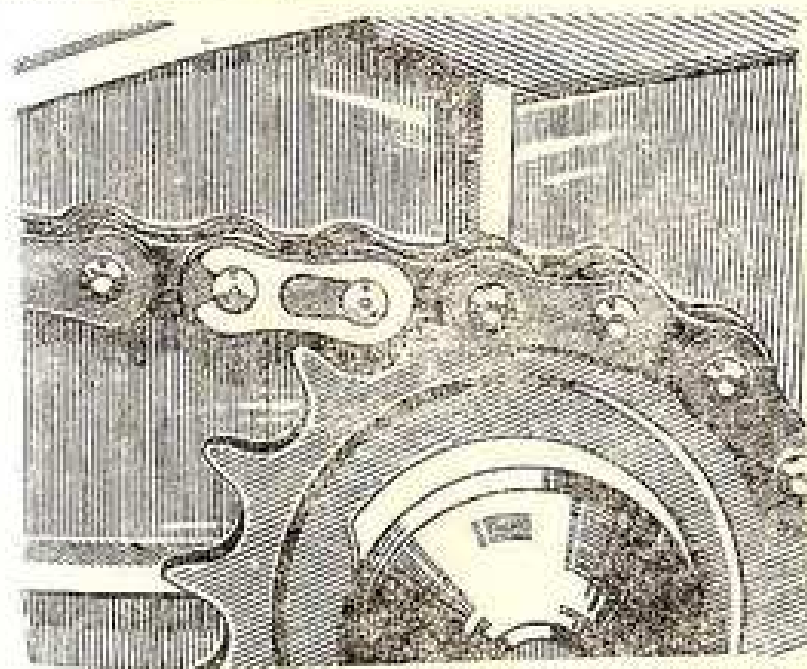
УСТАНОВКА ЗАЩЕЛКИ ЗАМКА ЦЕПИ
